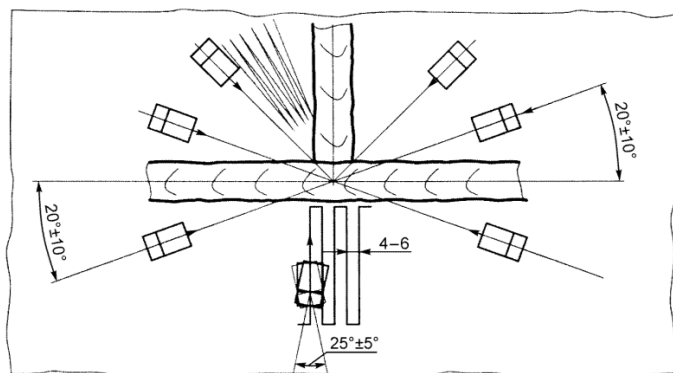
Схемы прозвучивания мест пересечений стыковых сварных соединений
